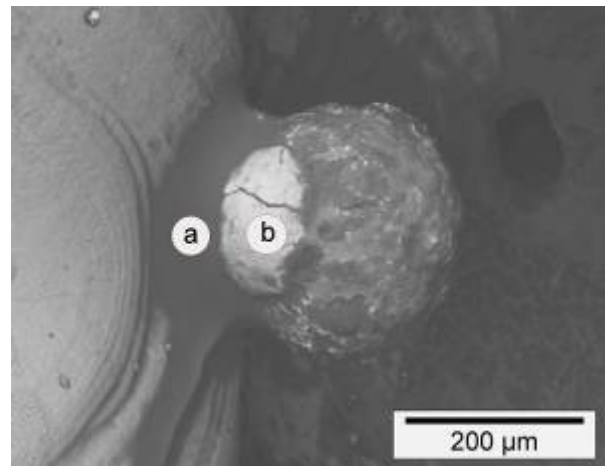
REM-Detailbild einer „Schweißperle“ aus Bild 65, rechter Bereich (BSE-Kontrast)
